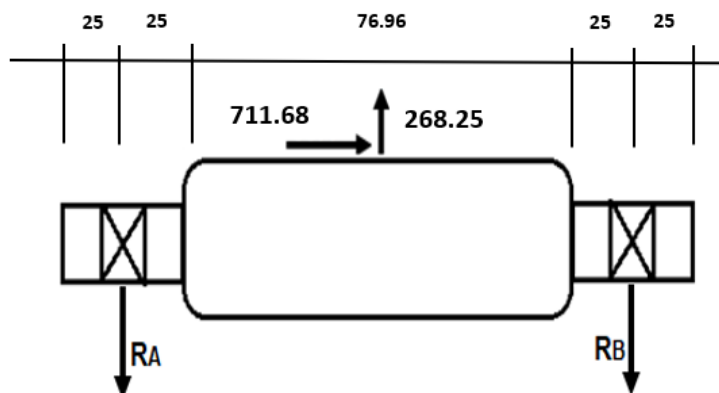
31. Fuerzas en los cojinetes sobre el eje del tornillo sinfín. Plano xy.
